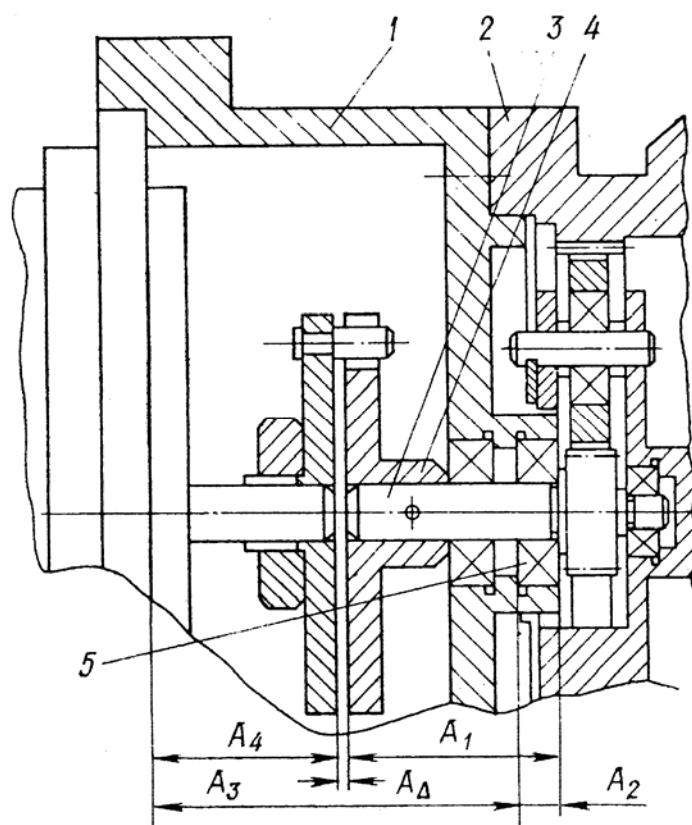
Узел подшипникового соединения: 1 – стакан; 2 – корпус; 3- вал; 4 – колесо; 5 – подшипник
